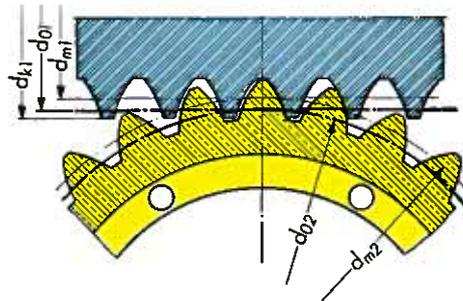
Hohlflanken-Verzahnung im Schneckenadsschnitt
